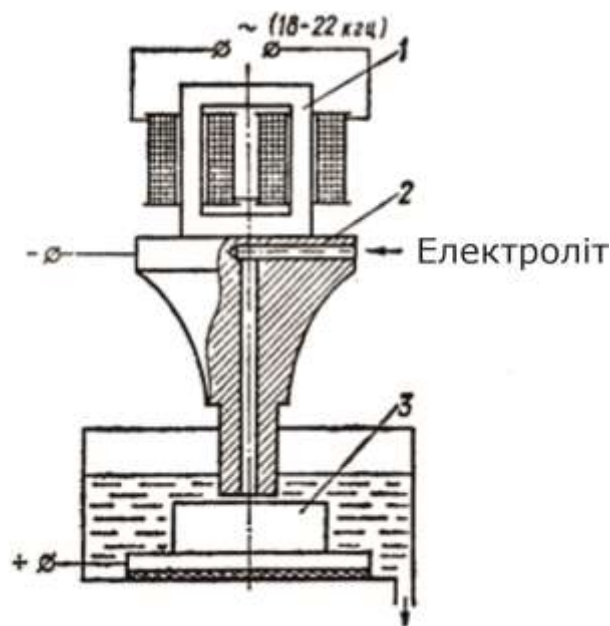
Схема ультразвукової електрохімічної обробки.
